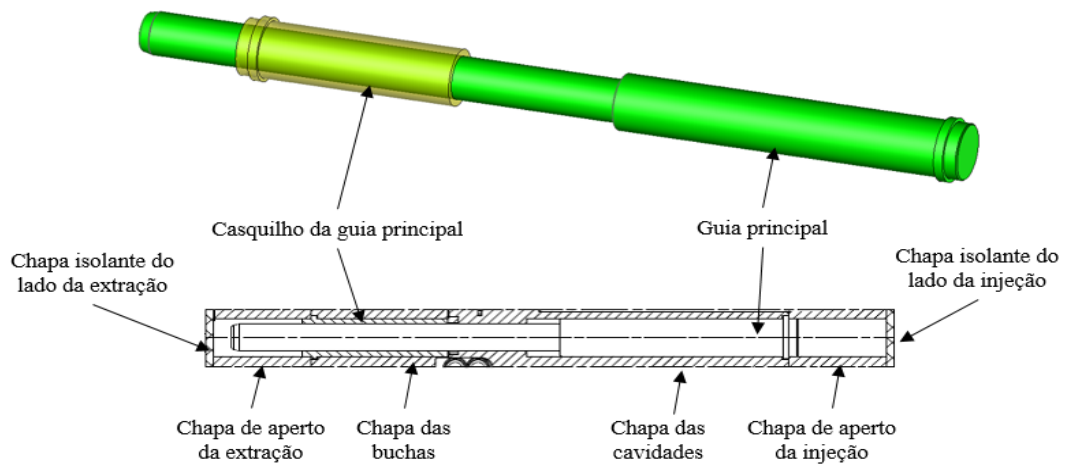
Conjunto de guias e casquilhos para guiamento do molde
